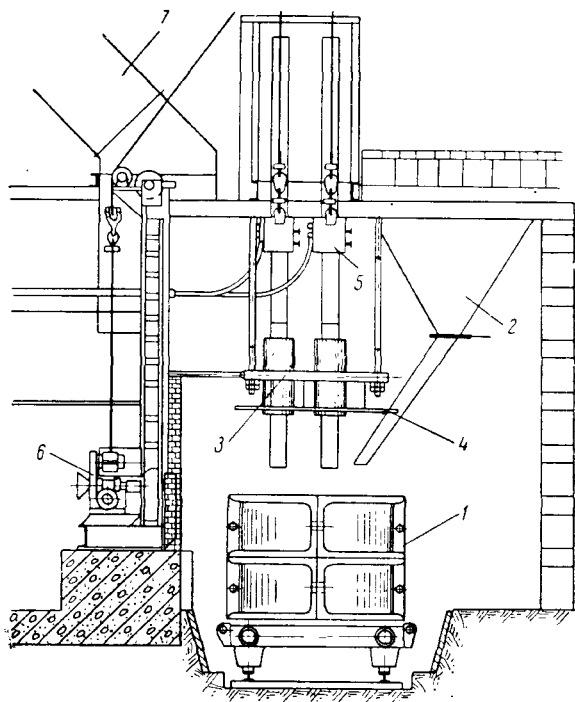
Электродной агрегат для выплавки металлического хрома с предварительным расплавлением части окислов (выплавка на блок):
